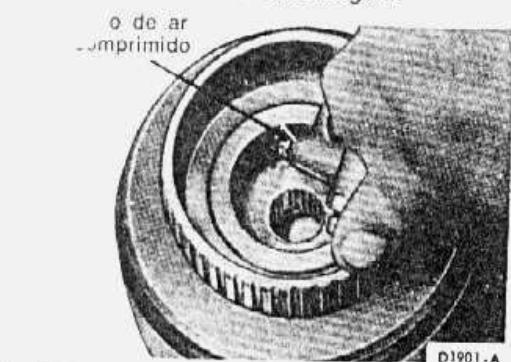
remoção do êmbolo da embreagem de marchas para frente
